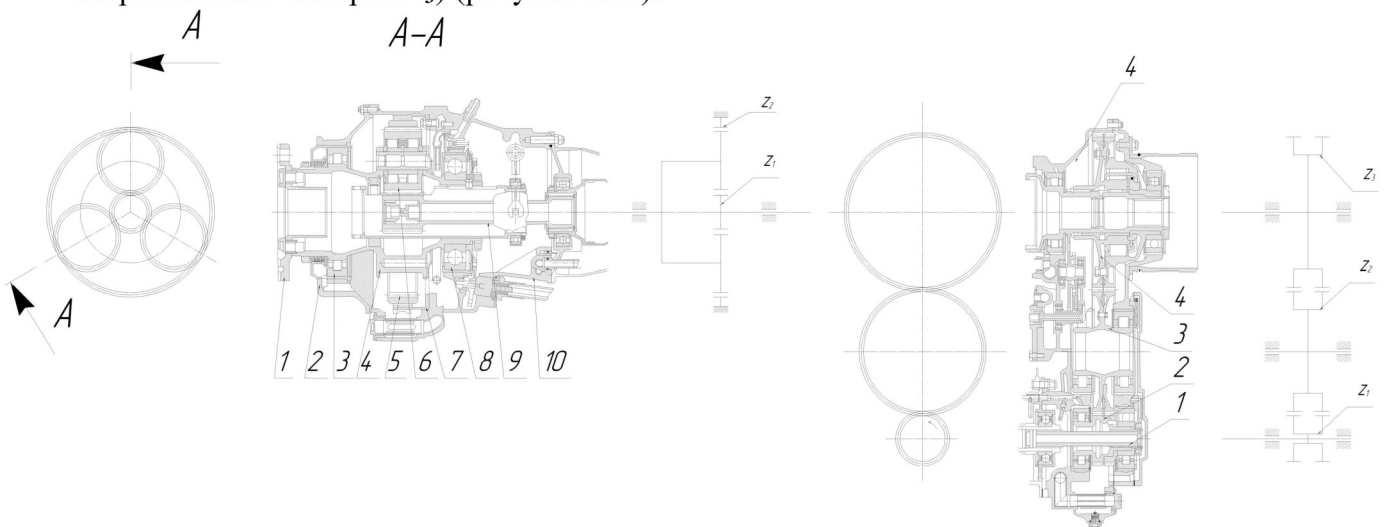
Двухступенчатый редуктор ТВД-10Б:
